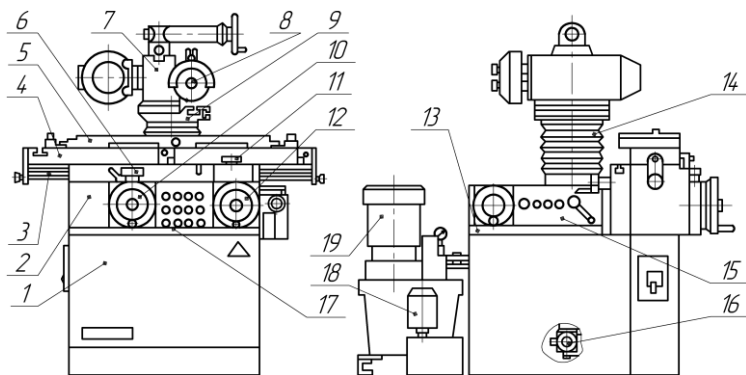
Компоновка универсально-заточного станка модели ЗД642Е
